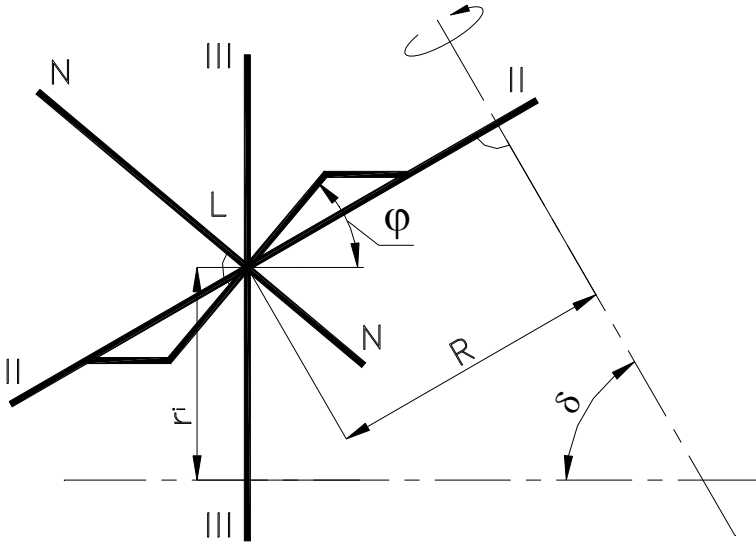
Визначення допустимого радіусу торцевої фрези для оброблення поверхні обертання
